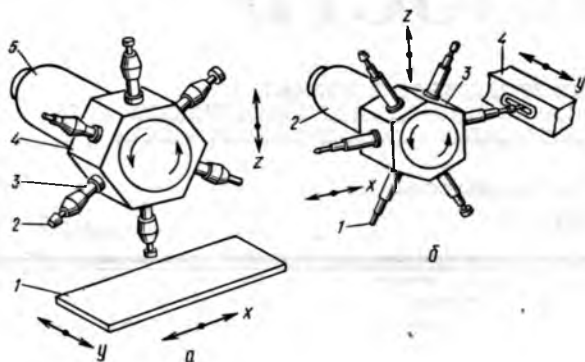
Револьверные инструментальные головки деревообрабатывающих станков:
